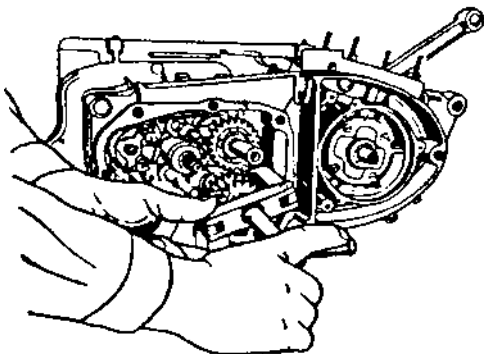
Выпрессовка промежуточного вала «Иж-П15»
